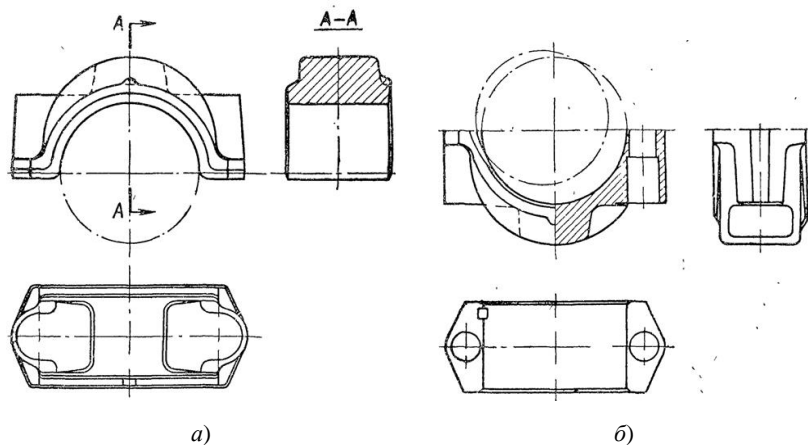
Штампованная заготовка крышки (а) и готовая крышка (б)
